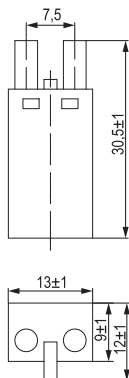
Габаритные и установочные размеры модуля / Figure 5 - Overall and mounting dimensions of the module / 5 сурет – Модулдің габариттік және орнату өлшемдері
